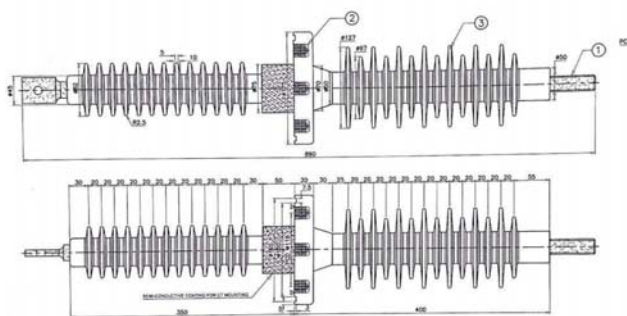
Креслення полімерного прохідного ізолятора в Autodesk AutoCAD
